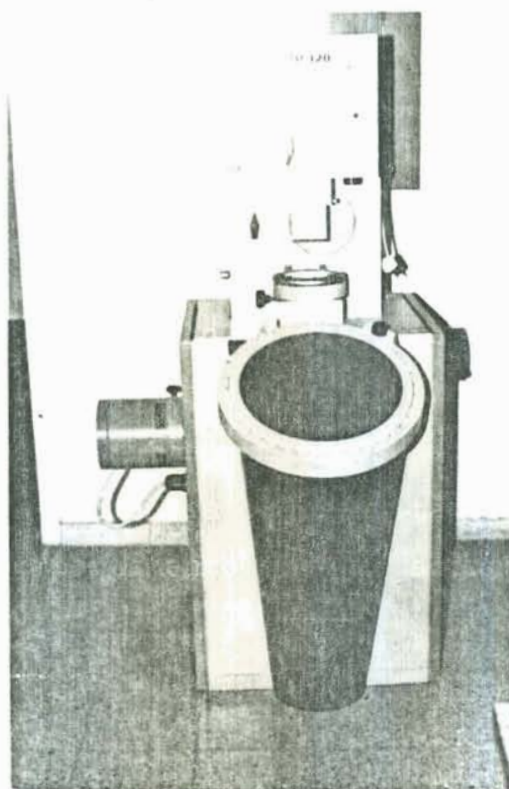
Equipamento utilizado para medições da profundidade de penetração e largura dos cordões de solda.
